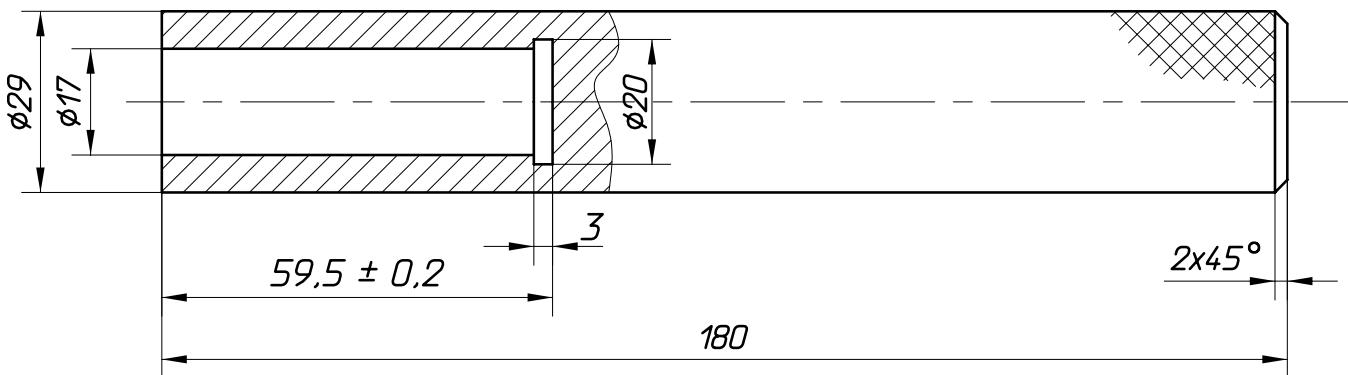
Оправка для запрессовки оси шкива в рычаг
